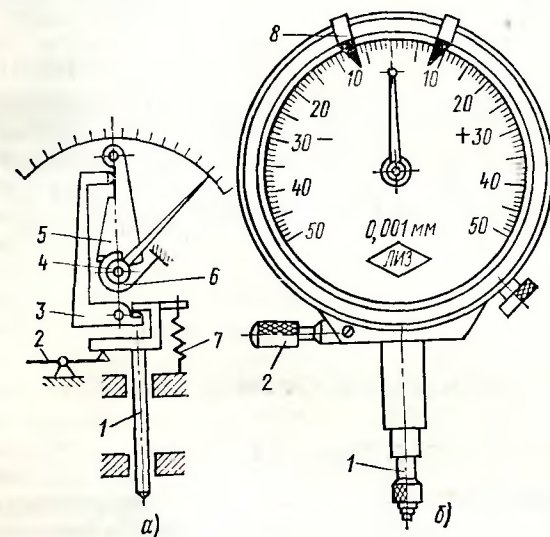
Рычажно-зубчатая измерительная головка: а — схема устройства, б — общий вид
